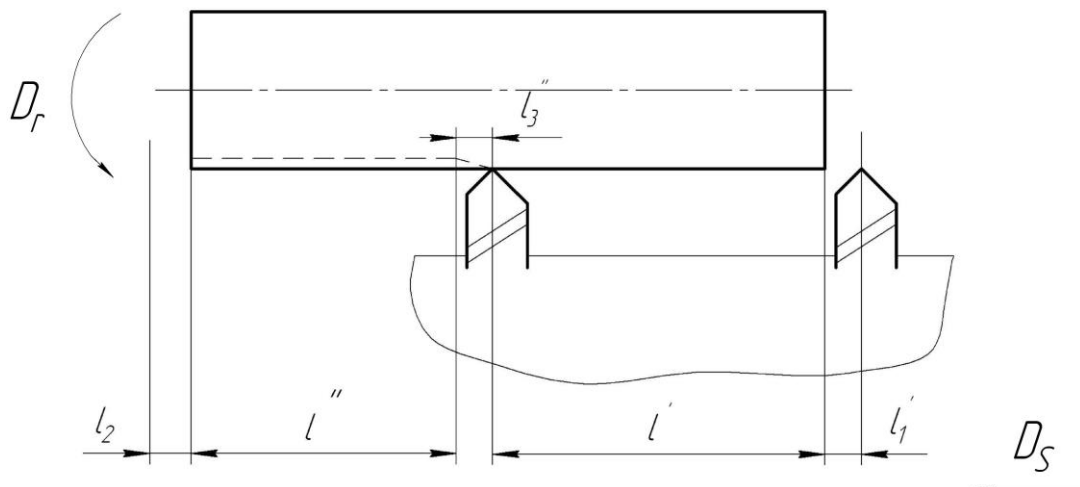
Схема обработки цилиндрической поверхности детали двумя резцами
